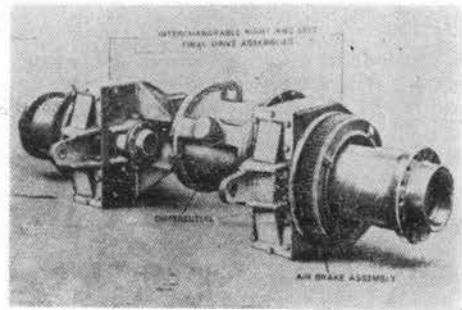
Le Tourneau-Westinghouse 社 Haulpak 用リヤアックスル
